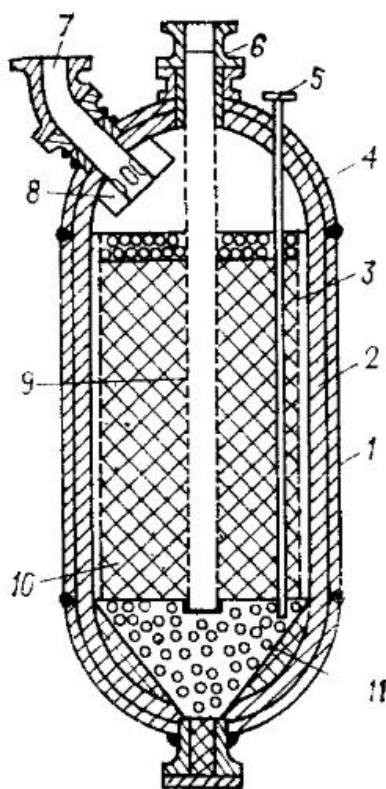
Реактор риформинга с радиальным вводом газосырьевой смеси [1]: 1 – корпус; 2 – футеровка; 3 – перфорированный стакан с сеткой; 4 – днище; 5 – штуцер для термопары; 6 – штуцер для вывода газо-продуктовой смеси; 7 – штуцер для
